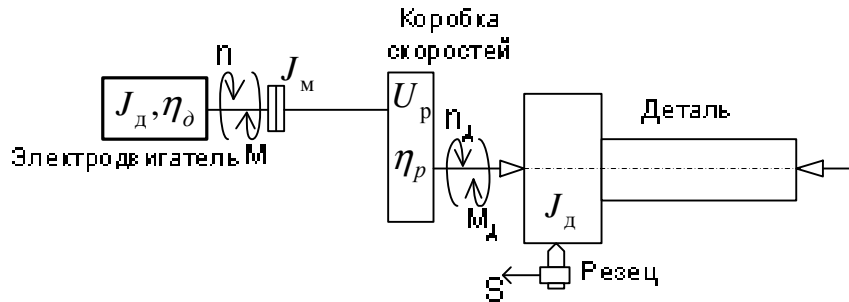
Упрощенная кинематическая схема привода главного движения токарного станка
